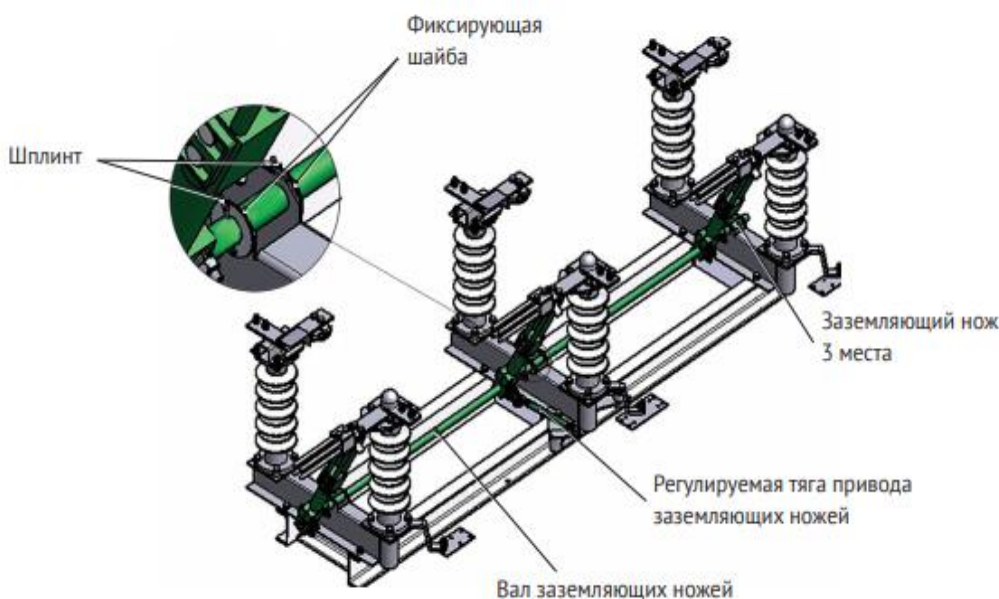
Главные и заземляющие ножи разъединителя
